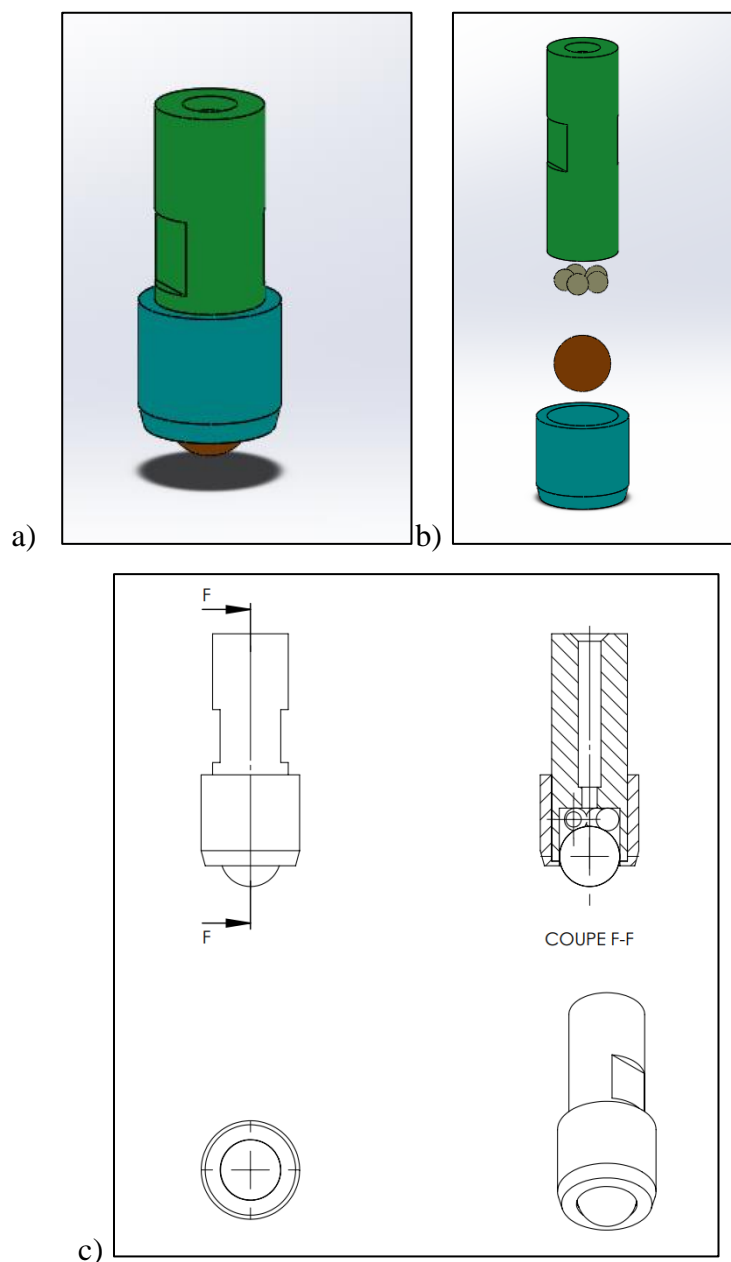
a) Vue en 3D de la tête porte bille 8 mm ; b) Vue éclatée ; c) Dessin d'ensemble de la tête porte bille \varnothing 8 mm
